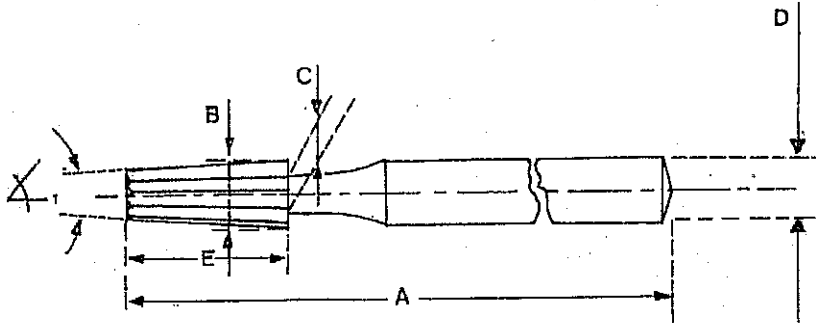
Fresa de carburo, forma de cono truncado (clave: 080.431.0460)
